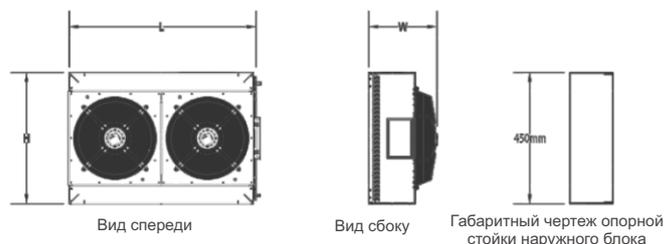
Конструктивный чертеж (с двумя вентиляторами)
